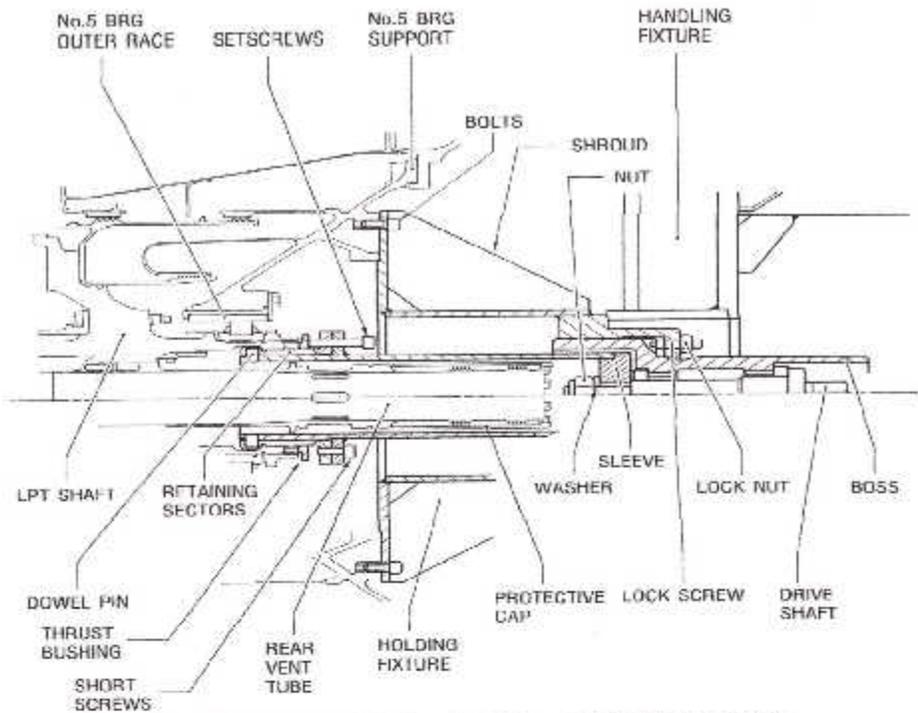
Installation du Dispositif.856A2618G03.
